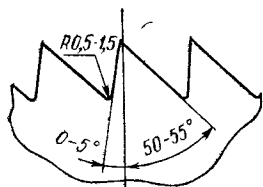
Форма и размеры зуба ножовочного станочного полотна
